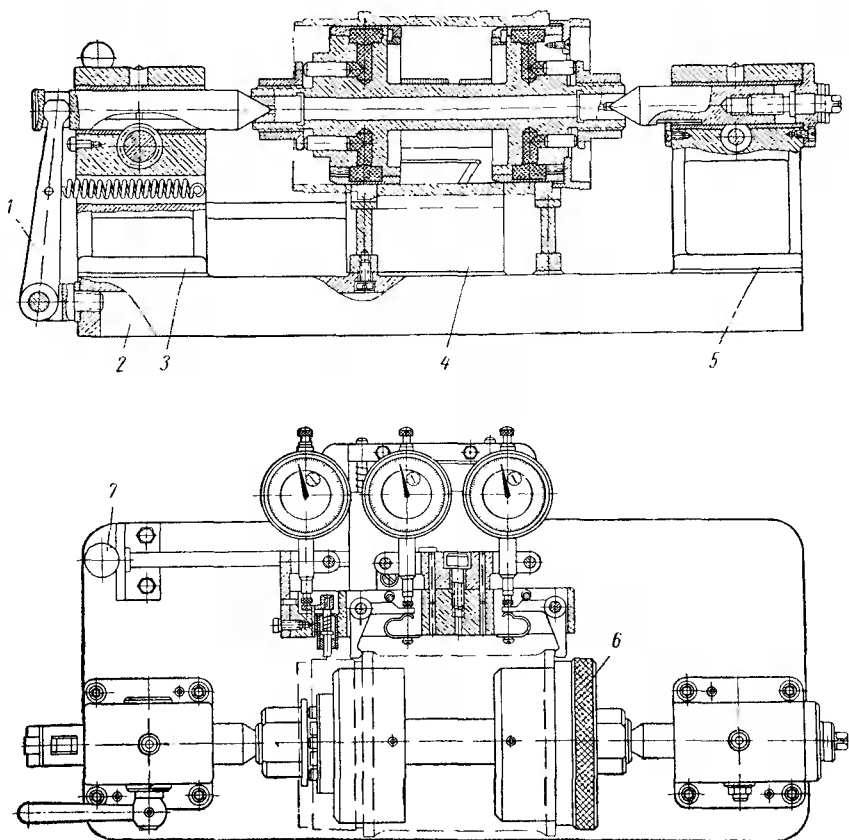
Приспособление для контроля точности обработки гильз цилиндров
